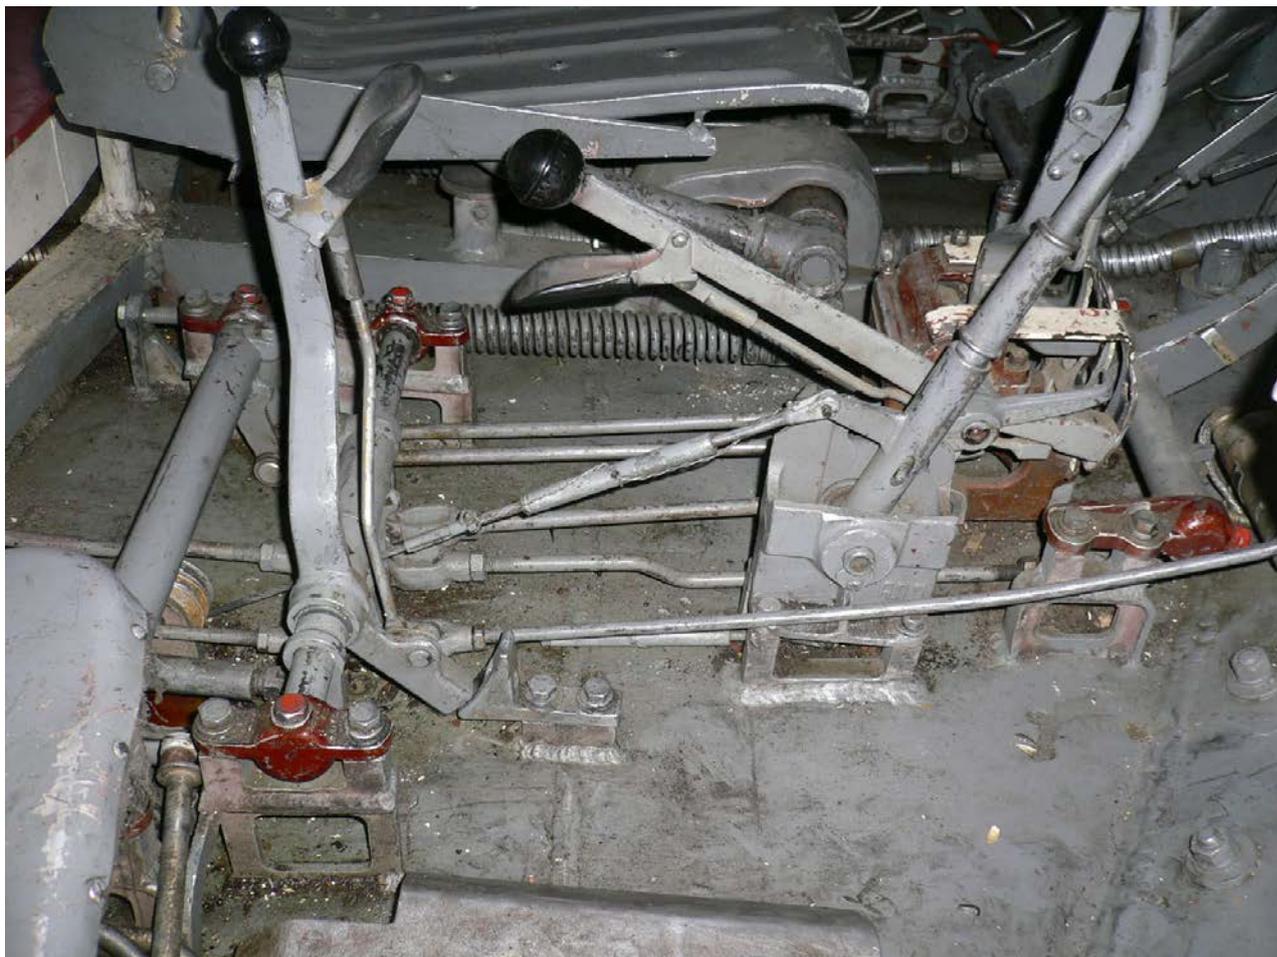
Приводы управления коробкой передач, главным фрикционом, бортовыми фрикционами механизма поворота и тормозами
